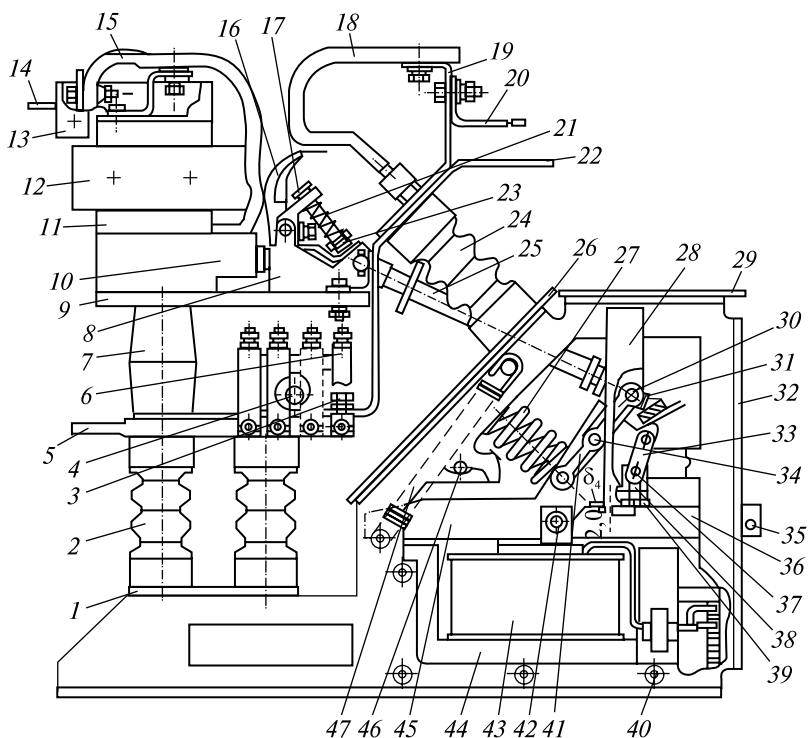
Быстродействующий выключатель ВАБ-49:
